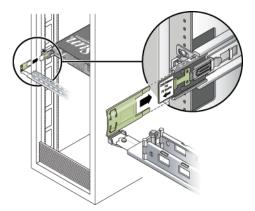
Collegamento del braccio di gestione dei cavi al connettore dell'estensione
